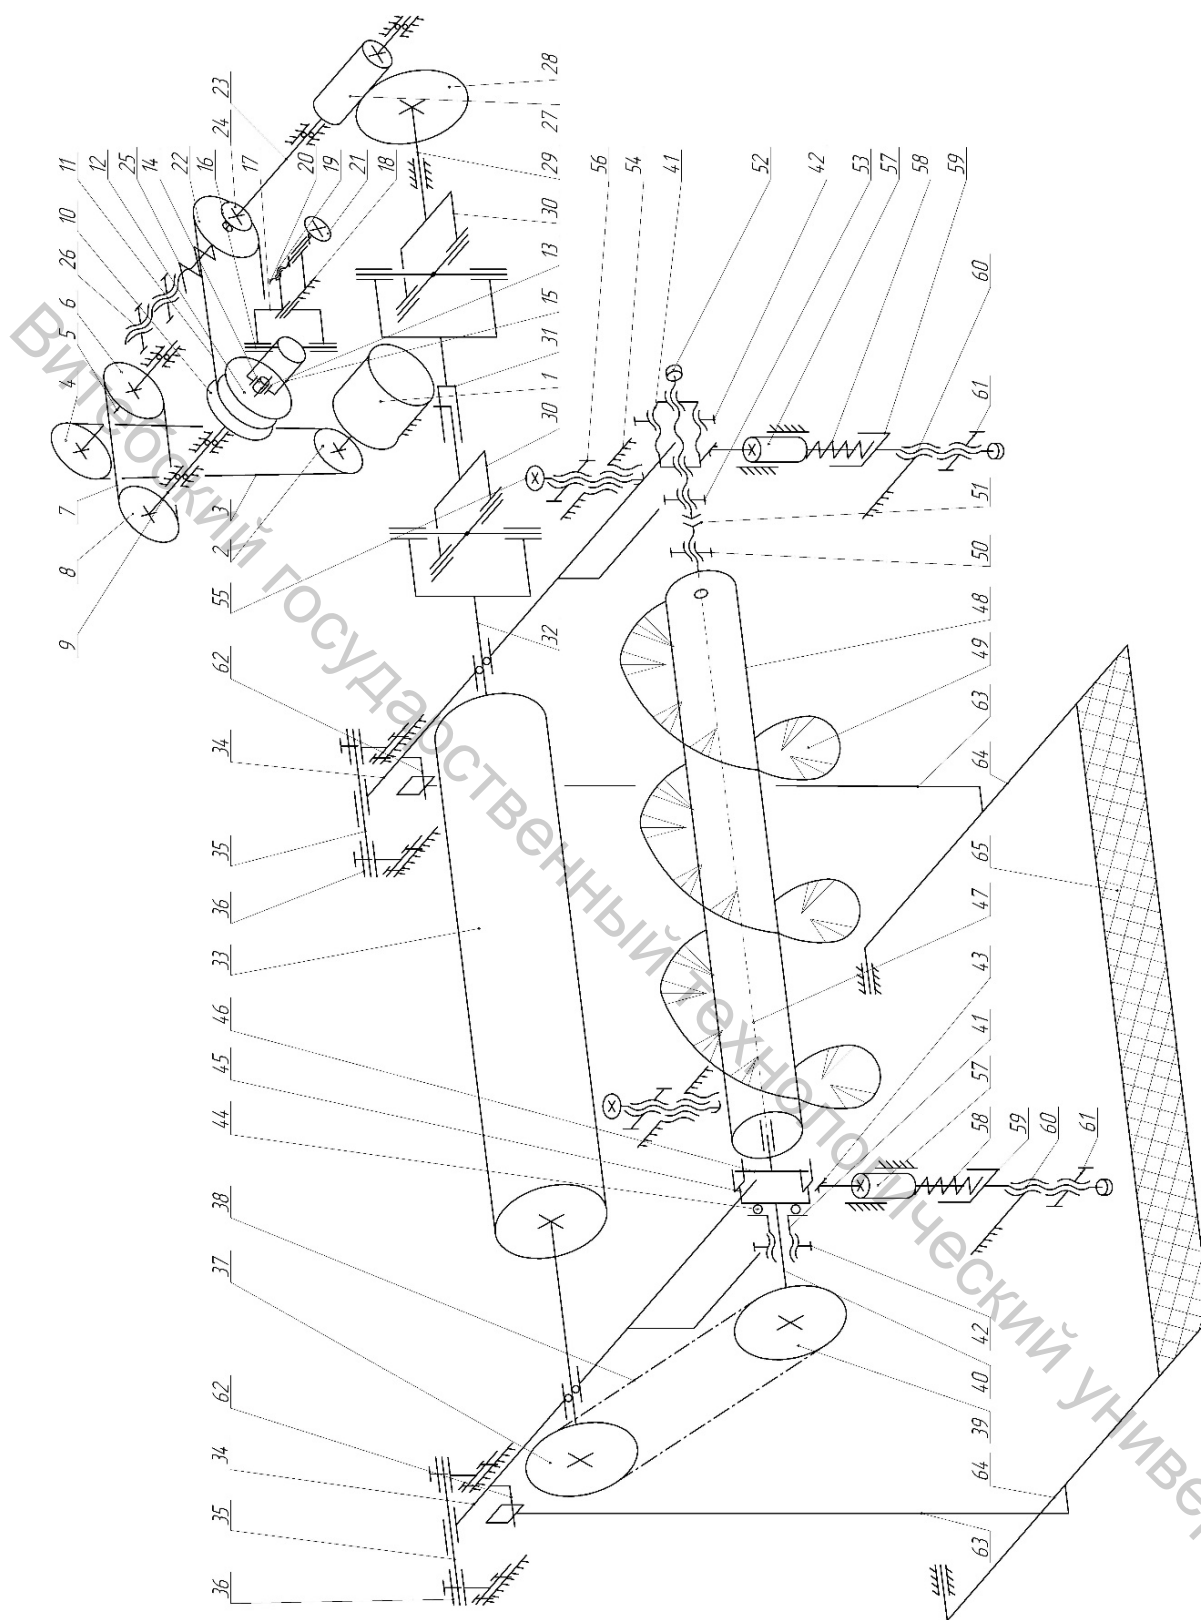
Кинематическая схема механизма транспортирующего
